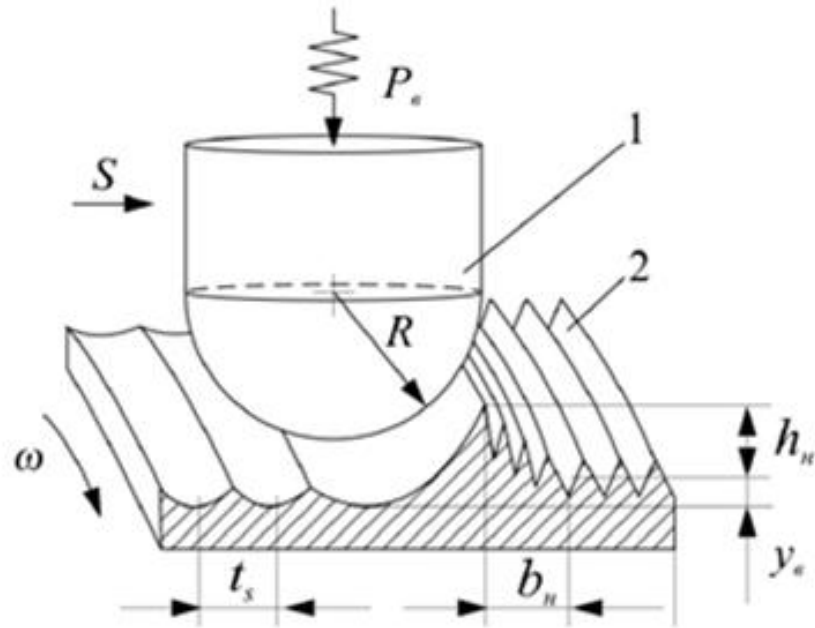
Схема выглаживания поверхности детали: 1- выглаживатель; 2- обрабатываемая поверхность;  $R$  – радиус выглаживателя;  $t_s$  – шаг подачи;  $\omega$  – угловая скорость детали [4]
